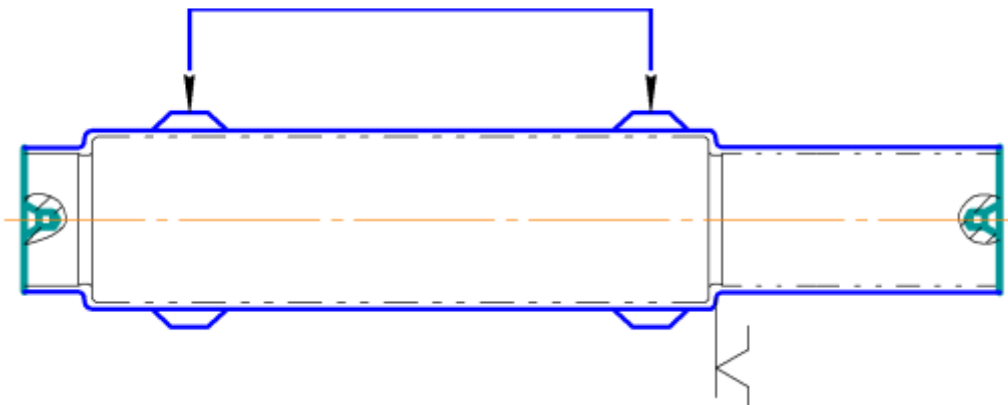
Схема базування при обробці вала на операції 020 (фрезерно-центрувальна)
